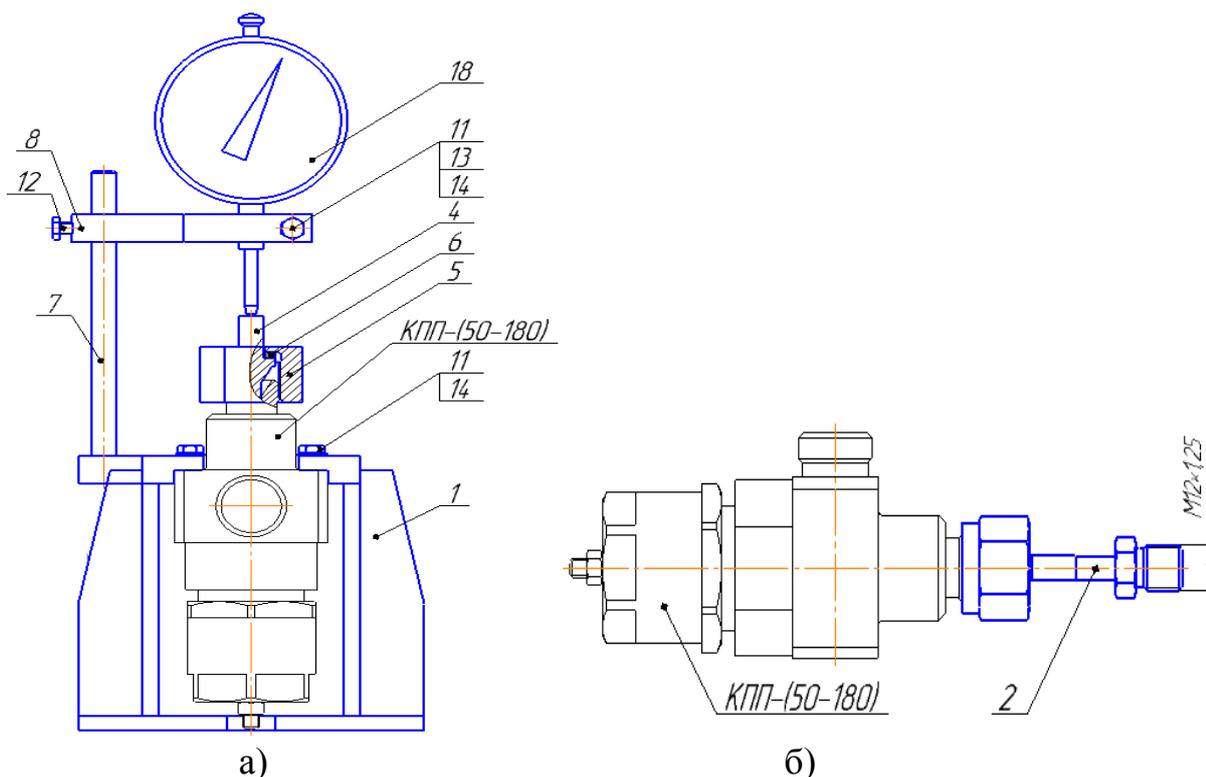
Схема испытаний и приспособления для проверки величины хода и срабатывания клапана КПП – (50-180). 1-каркас, 2- переходник сварной, 4-толкатель, 5-гайка, 6-шайба, 7-направляющая, 8-планка, 11,12-болты, 13-гайка, 14-шайба, 18-индикатор часового типа ИЧ10 кл.1 ГОСТ 577-68.
